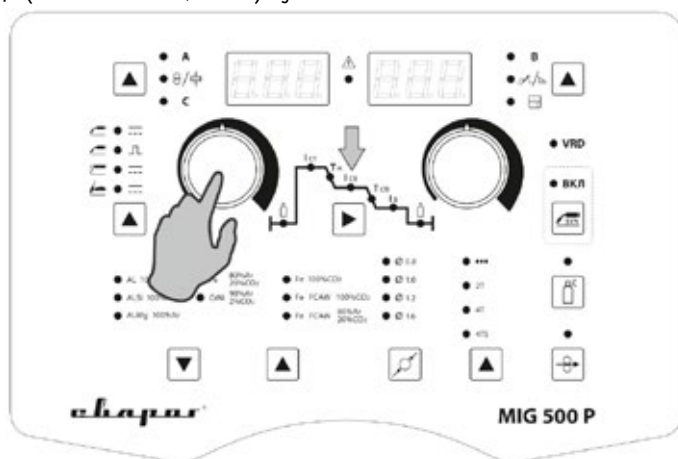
Регулятор силы сварочного тока.
